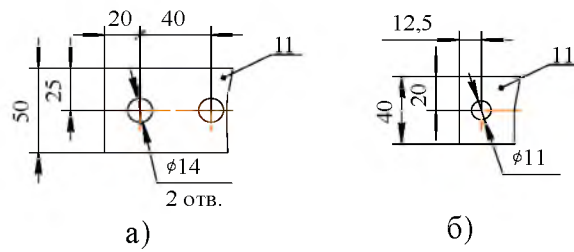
Контактный вывод разъединителя со стороны подвижной колонки:
